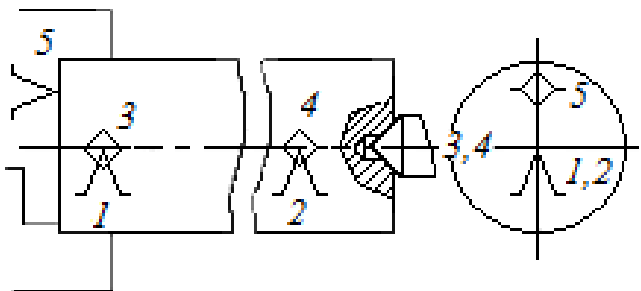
Установка вала в 3-х кулачковому патроні і центрі
